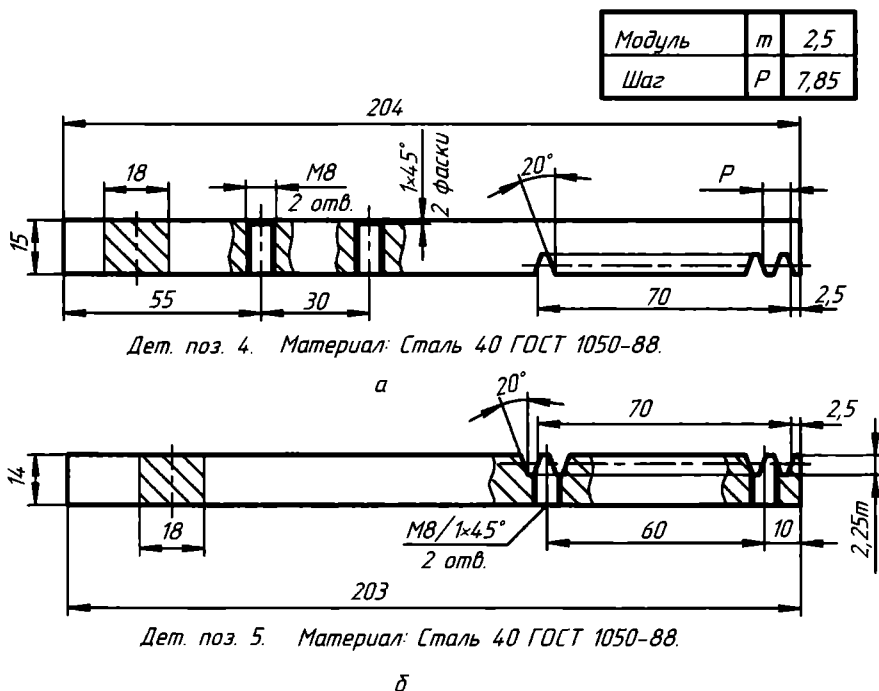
Чертежи реек: а — левой тарелки; б — правой тарелки
